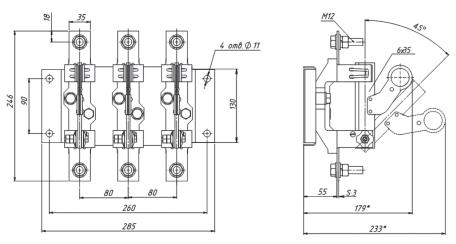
Разъединитель Р103 с пополюсным оперированием штангой ШО-1 на номинальный ток 1000 A
